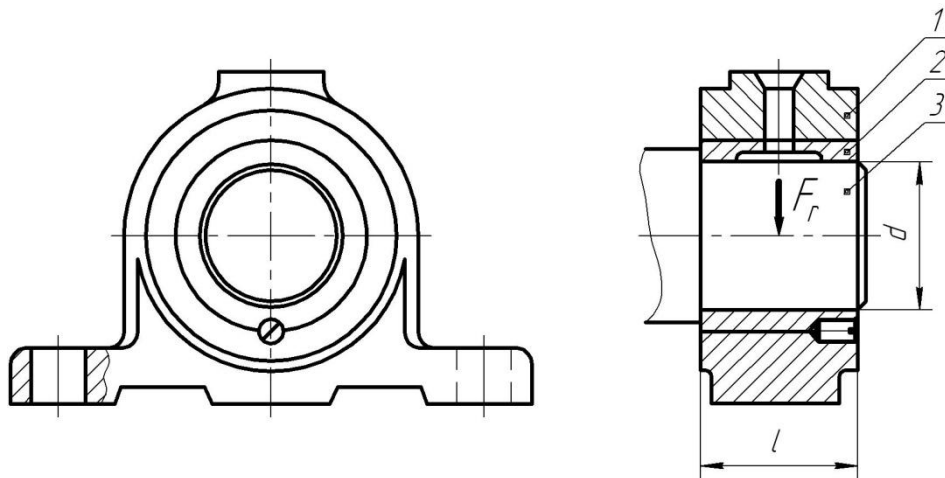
Конструкція радіального підшипника ковзання
